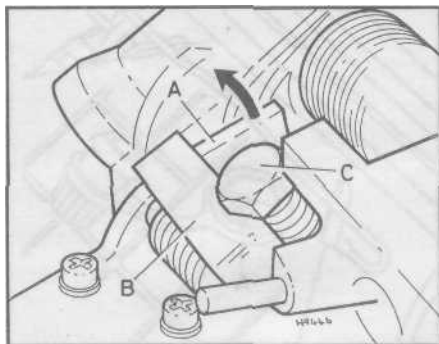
Проверка регулировки ускорительного насоса, указывающая рычаг прогрева двигателя (А), рычаг (В) и болт (С)
